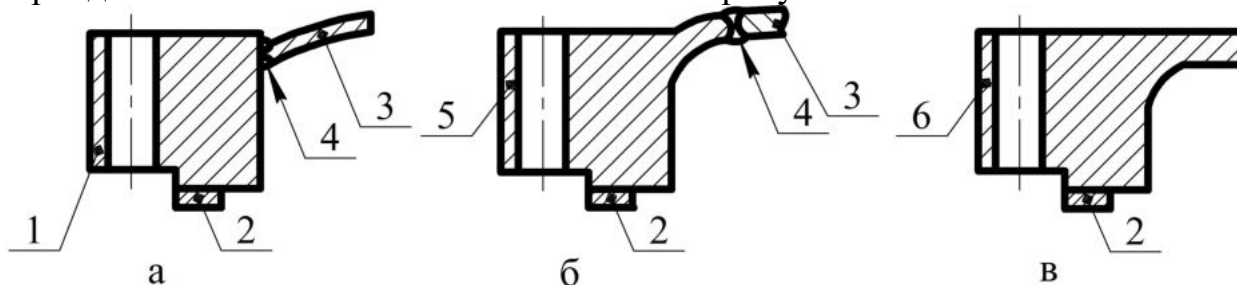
Типові конструкції кришок плаваючих головок: а – кільце-днище; б – фланець-днище; в – суцільна конструкція; 1 – кільце; 2 – прокладка; 3 – днище; 4 – зварний шов; 5 – фланець; 6 – суцільна механічно оброблена кришка
